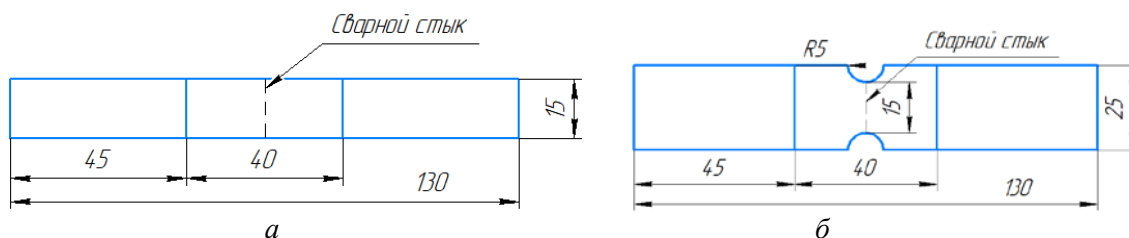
Образцы сварных соединений для механических испытаний на растяжение по ГОСТ 6996: а) тип XV; б) тип XXIV
